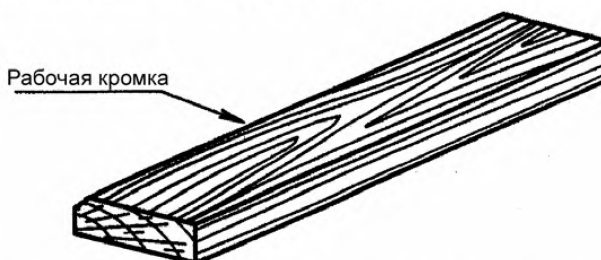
Фрезерование на упоре (обрабатываемый край)
